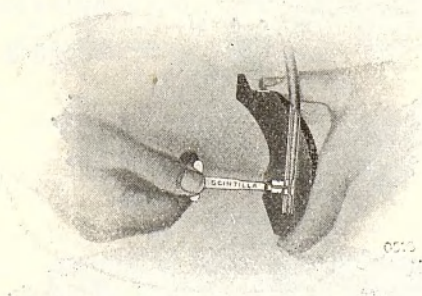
Atornillaje del tornillo de punta en los portacables para la fijación de los cables
